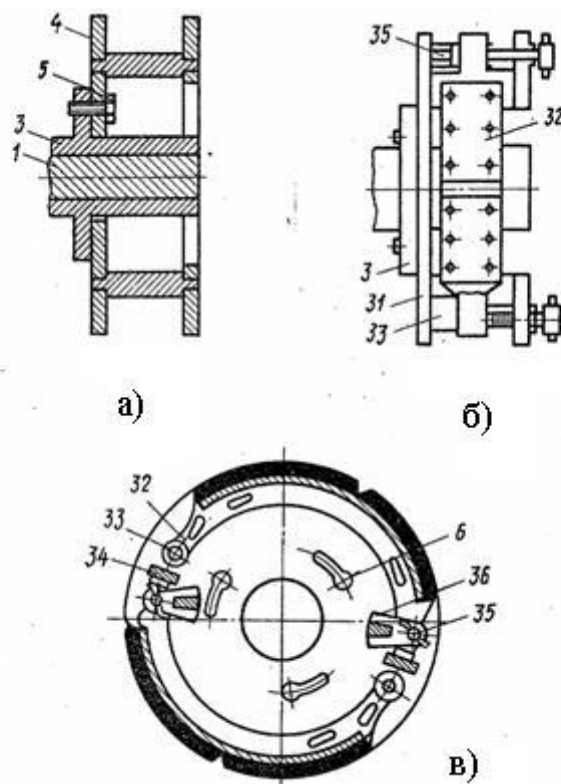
Схема крепления поворотной крепежной площадки и поворотная крепежная площадка для установки тормозной колодки
